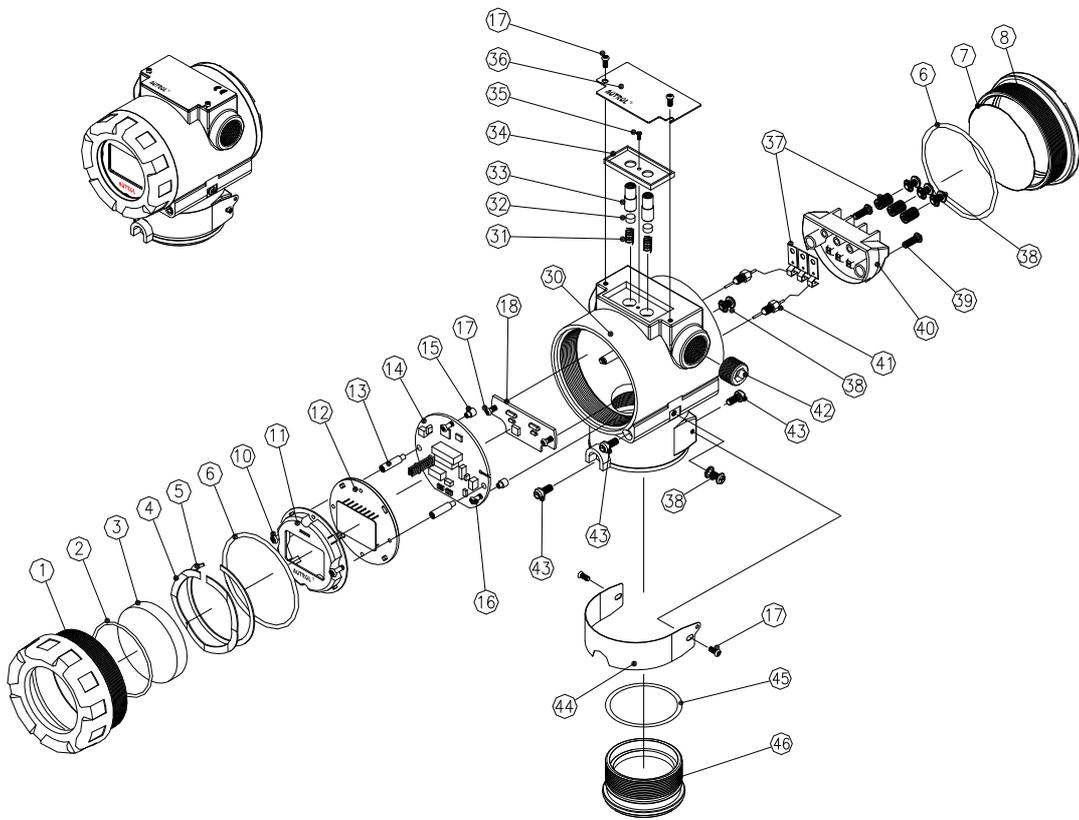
Model AI-100 Indicator Exposed View (Housing)
